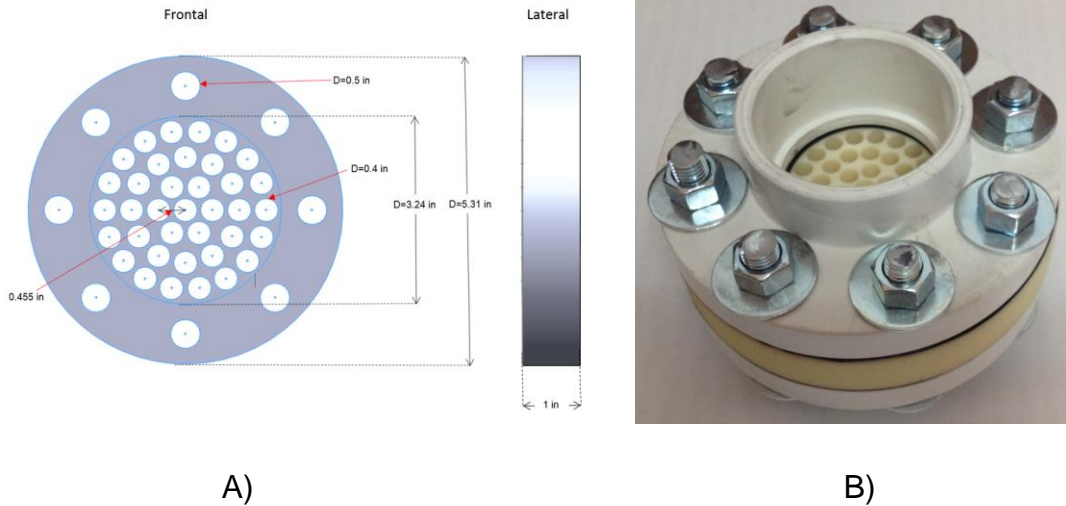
Enderezador de flujo. A) Dimensiones y distribución de orificios, B) Elemento manufacturado, acoplado y sujetado con bridas.
